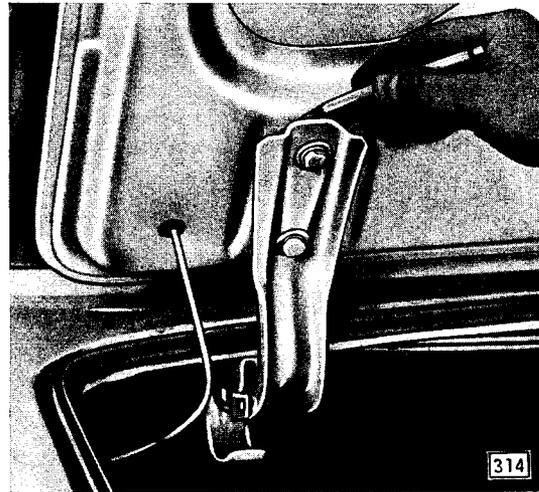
Lage des Kofferraumdeckelscharniers am Kofferraumdeckel markieren
